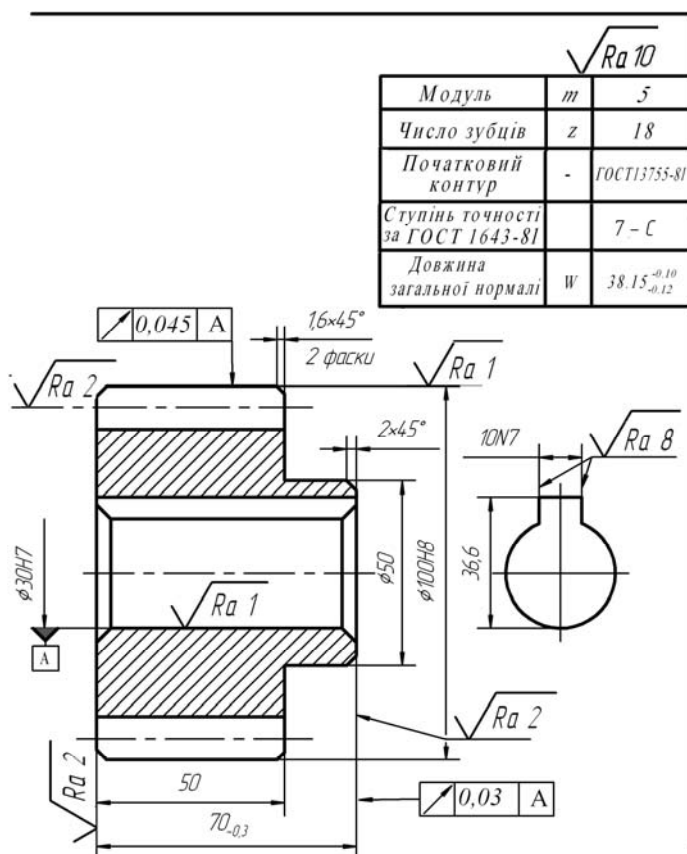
Приклад робочого кресленика циліндричного зубчастого колеса з прямими зубцями
